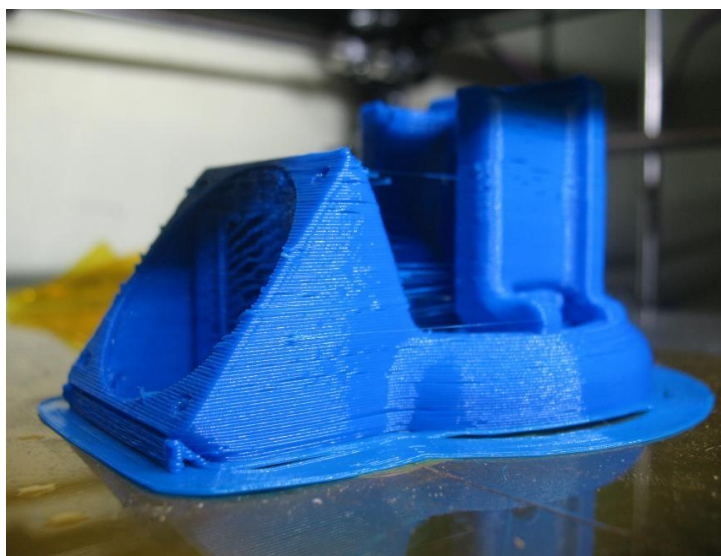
Корпус двигателя с патрубком, из материала PETG
